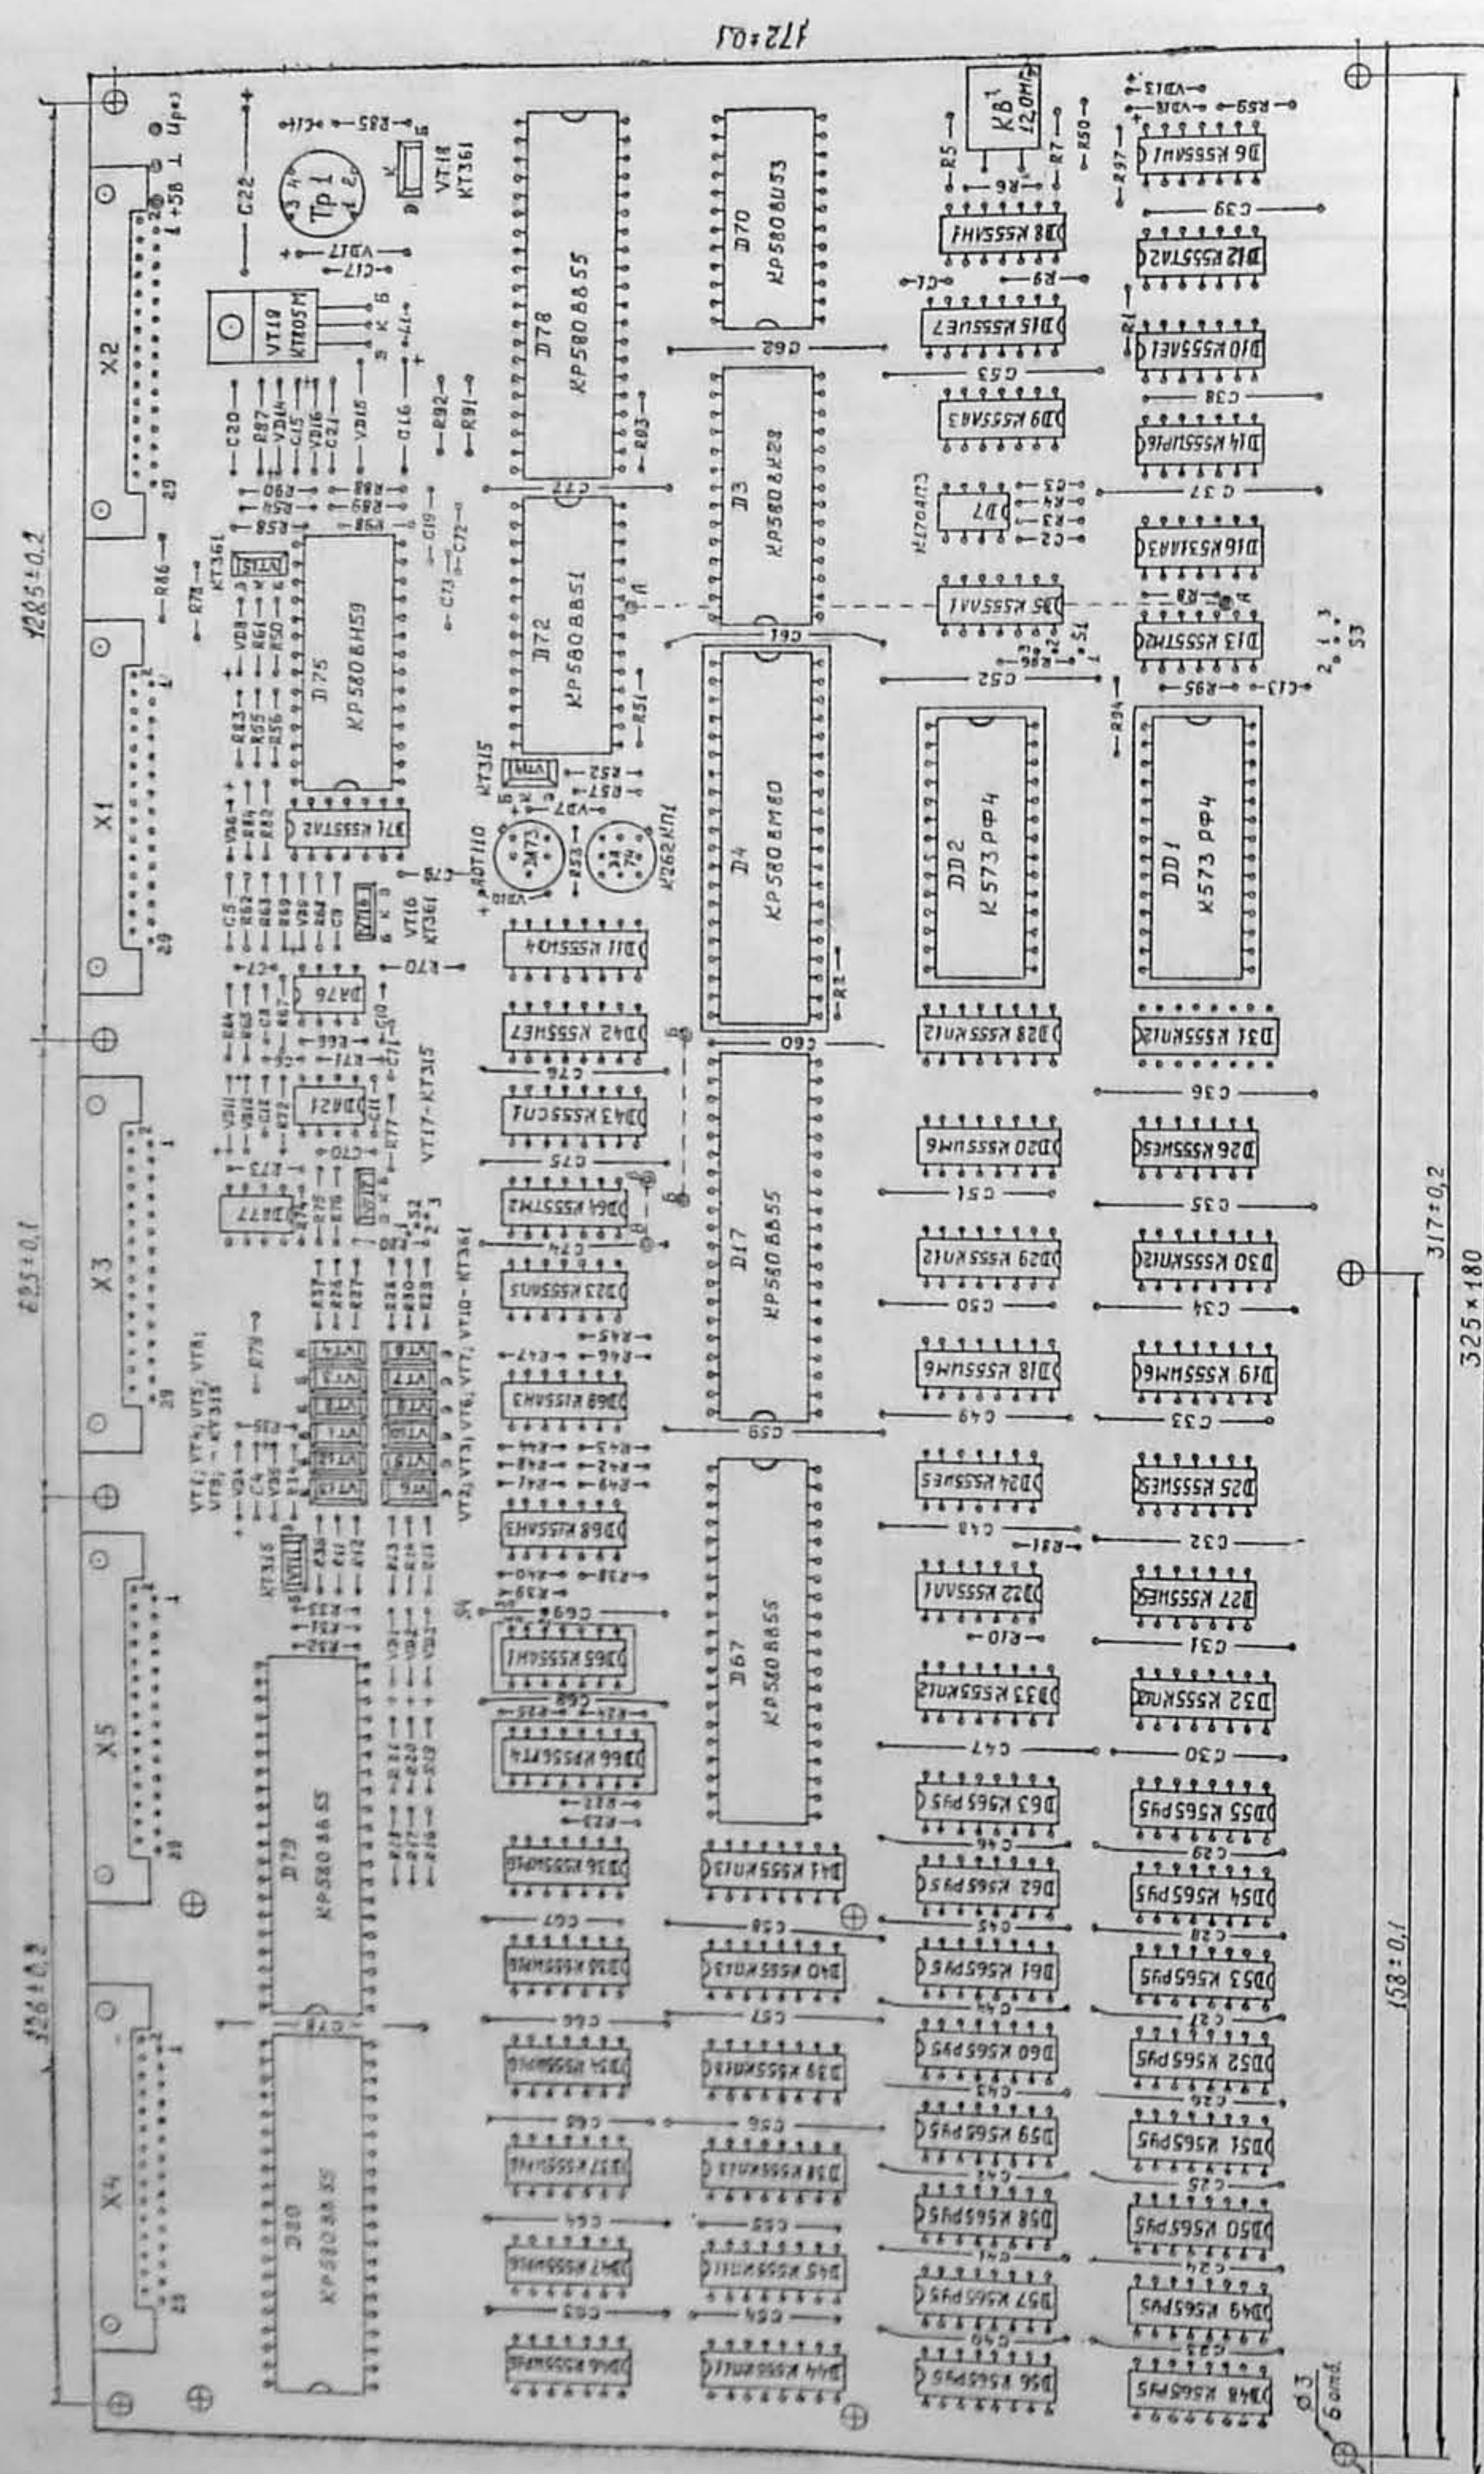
Сборочный чертеж печатной платы ПЭВМ
